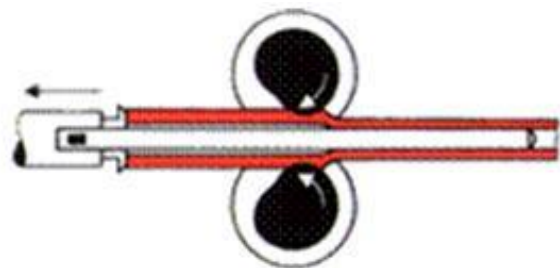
Схема холодної пільгерної прокатки труб (ХПТ)
